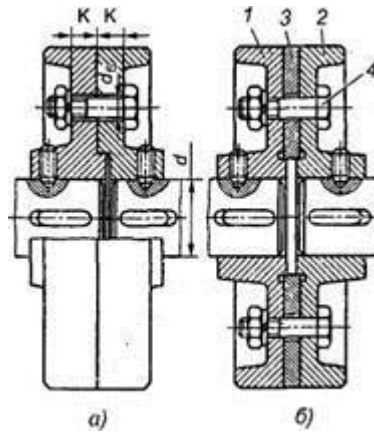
Фланцевые муфты: *а* - центровка за счет выступа; *б* — центровка кольцом
